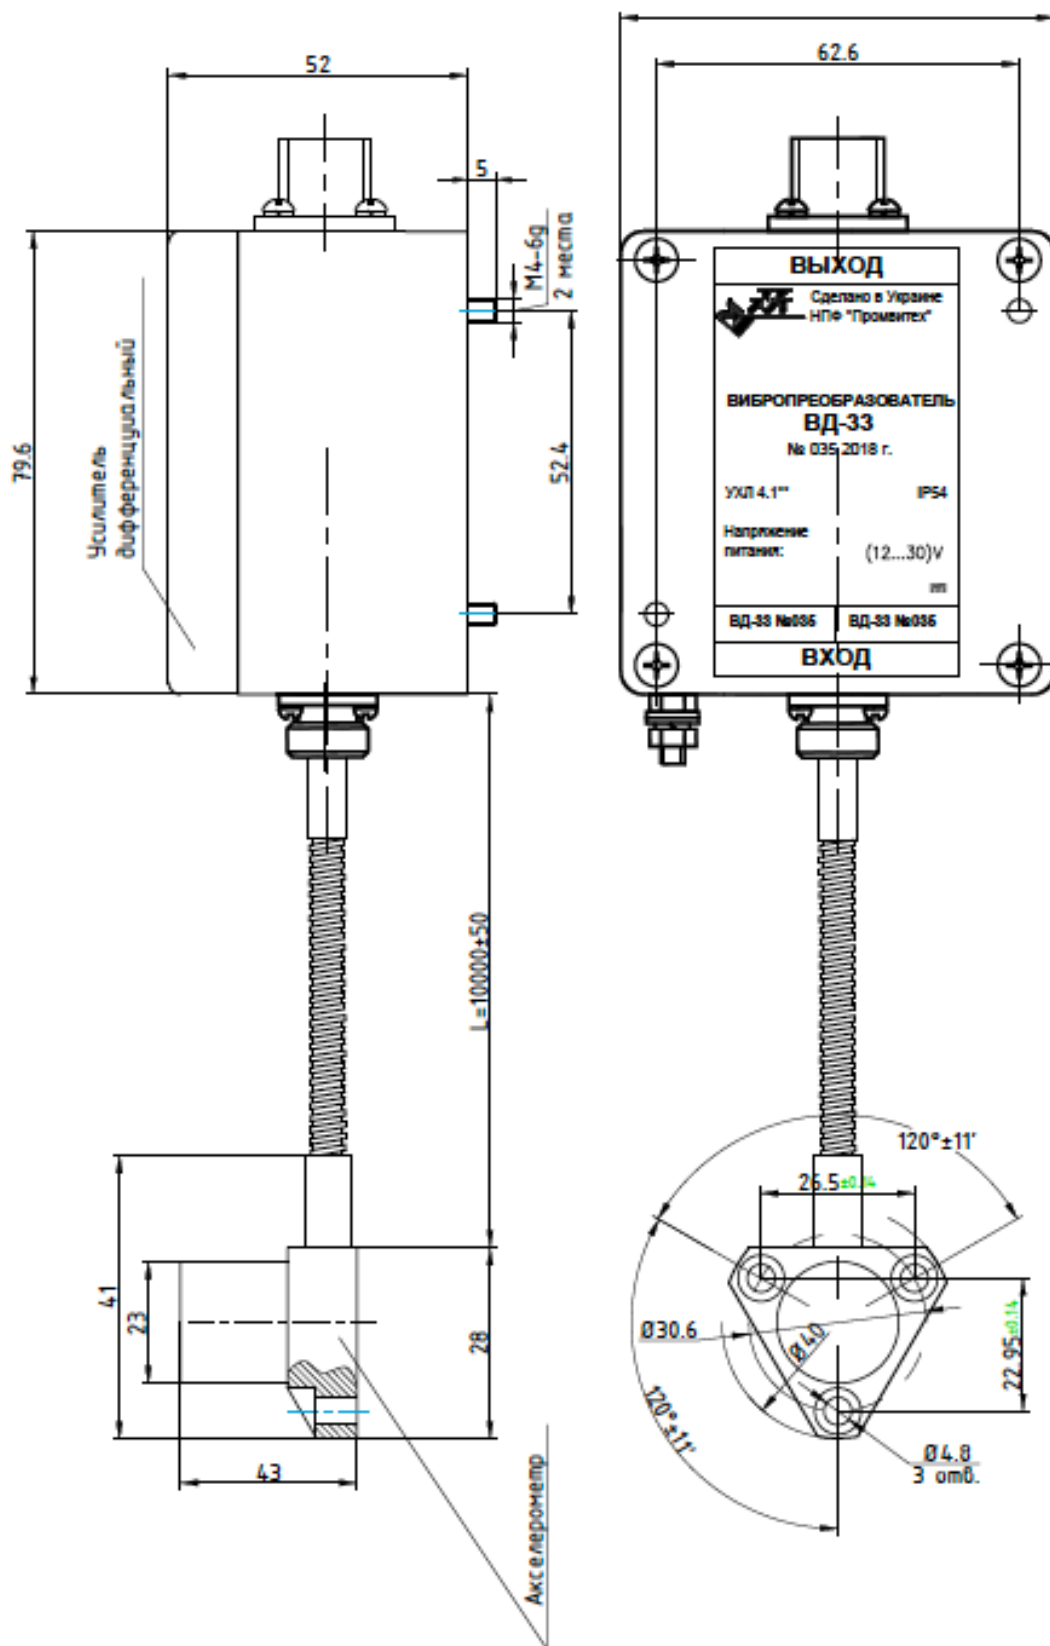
Габаритные и установочные размеры вибропреобразователя ВД-33
